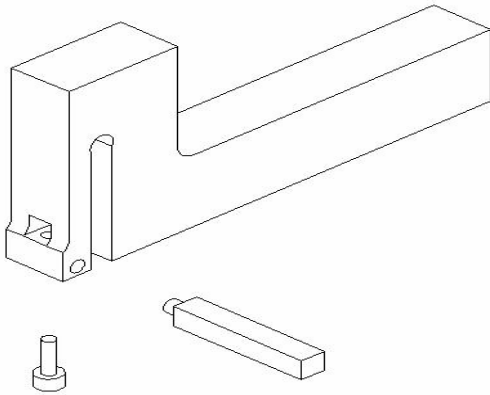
Vista isométrica del dinamómetro para medición de la fuerza de corte en torneado.
